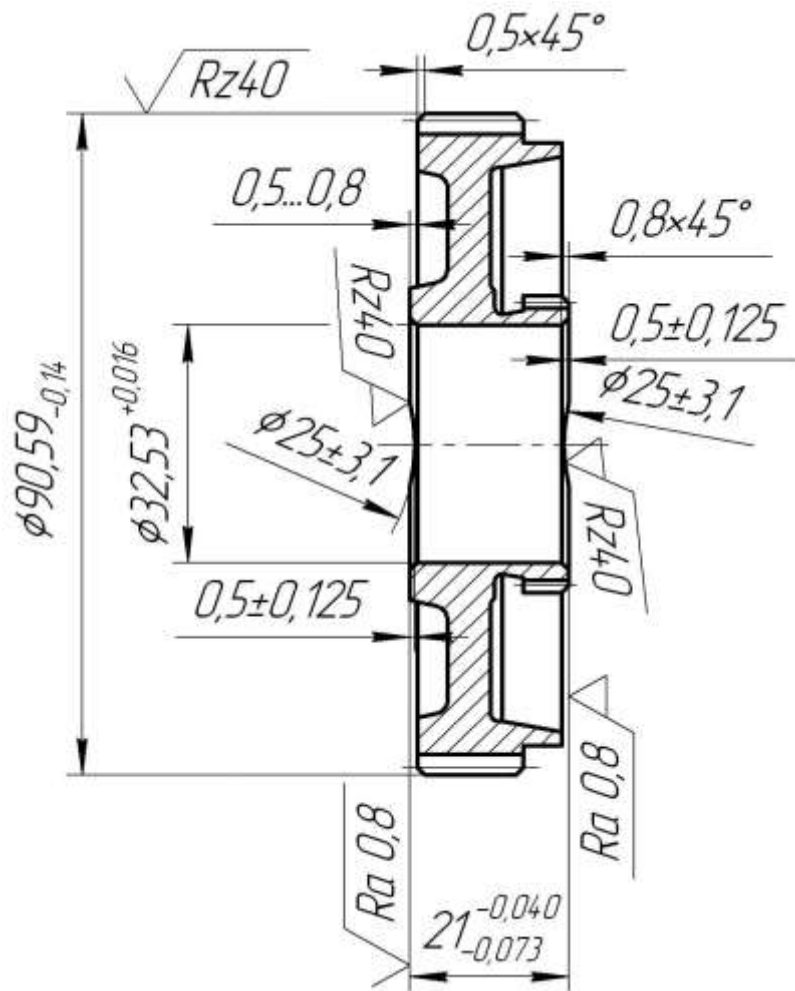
Шестерня ведущая 5-й передачи (деталь)
